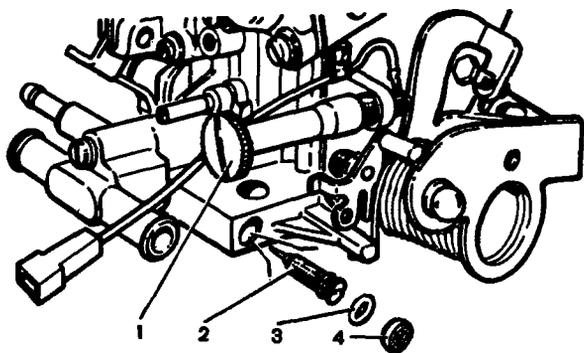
Винты регулировки системы холостого хода карбюратора 21053-1107010: 1 - регулировочный винт количества смеси; 2 - регулировочный винт качества (состава) смеси; 3 - уплотнительное кольцо; 4 - заглушка регулировочного винта
